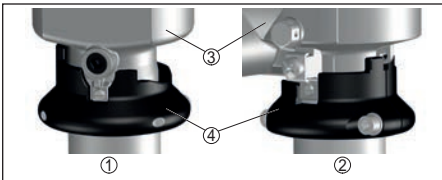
Gehäusearretierung beim Edelstahl-Feingussgehäuse
